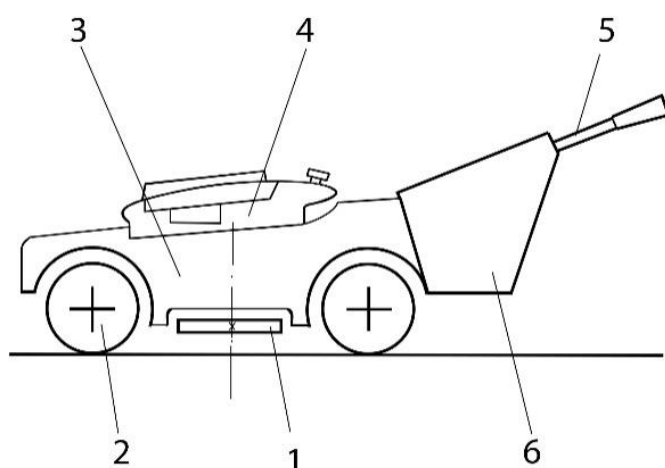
Газонокосилка VikingMB – 650T: 1 – рабочий орган (нож); 2 – ходовая часть; 3 – корпус; 4 – двигатель; 5 – рукоятка управления; 6 – травосборник.
